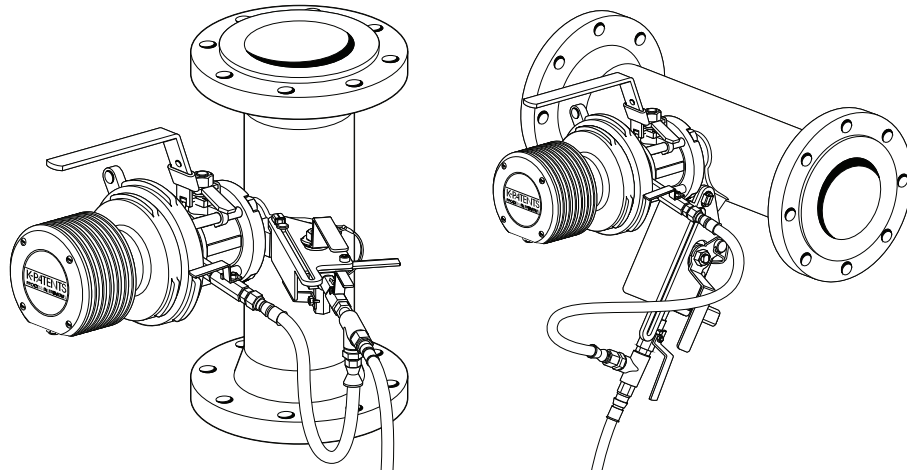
Montajes de la pieza de tramo de tubería vertical y horizontal (sistema de lavado con vapor)
